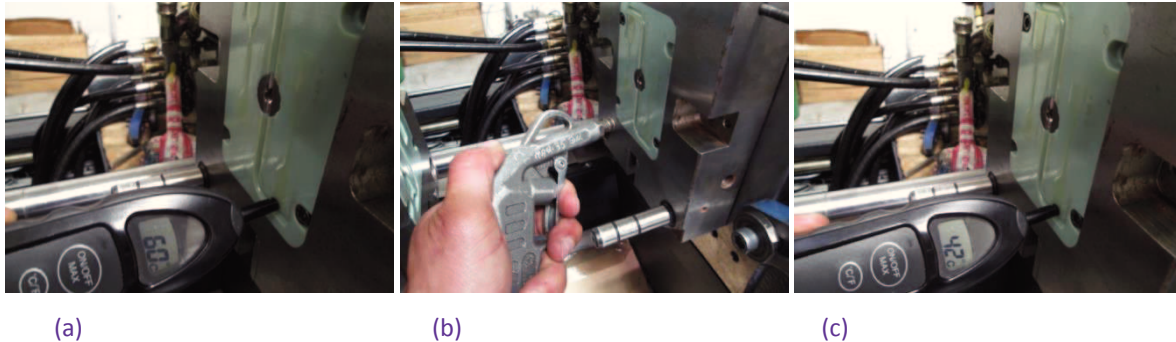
a) Temperatura após extração da peça injetada; b) Aplicação de ar comprimido no arrefecimento superfícies moldantes, durante 7 segundos; c) Temperatura das superfícies moldantes após arrefecimento
